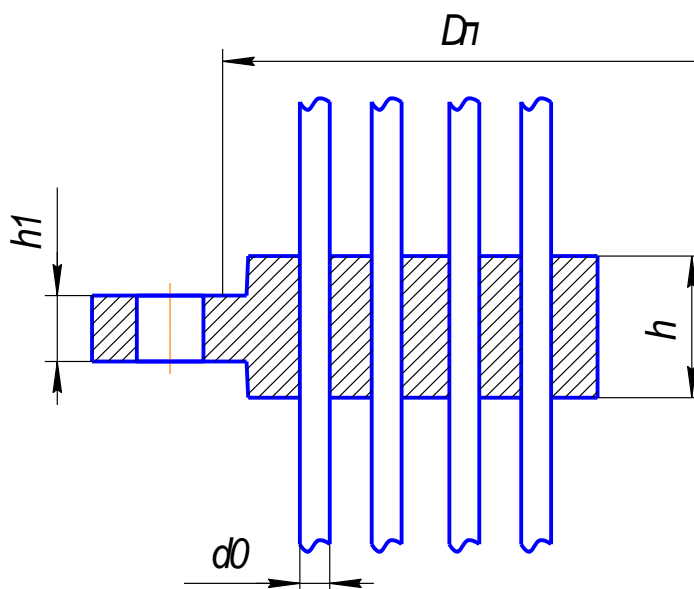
Конструкція трубної решітки, тип I (апарат з нерухомою трубною решіткою)
